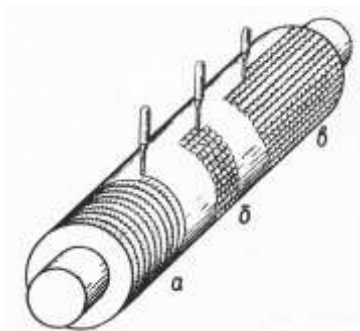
Схема наплавлення тіла обертання: а – по гвинтовій лінії; б – вздовж твірної; в – вздовж твірної окремими валиками
